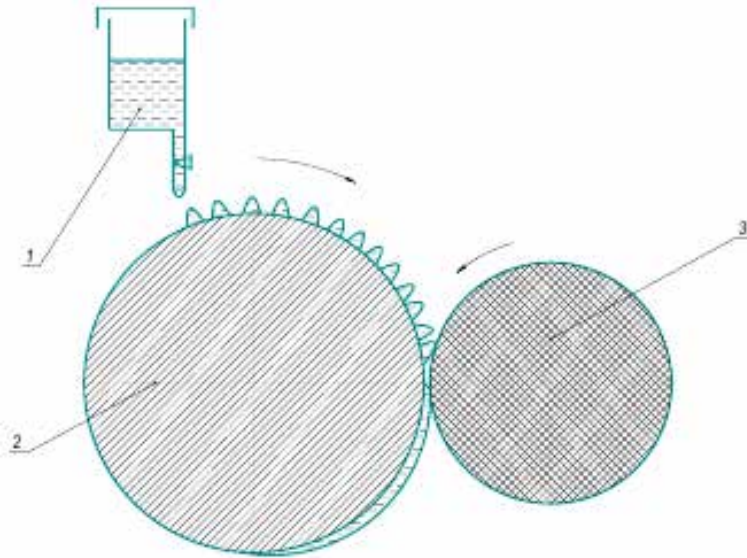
Спосіб нанесення полімерного покриття на деталі типу «вал»: 1 - резервуар; 2 - деталь; 3 - фторопластовий ролик.
